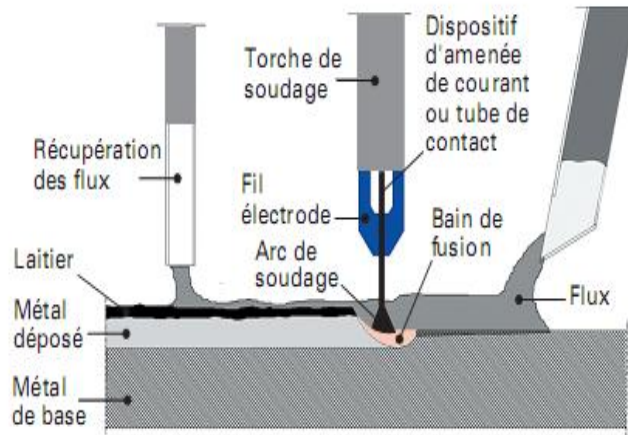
Procédé de soudage à l'arc électrique sous flux solide
